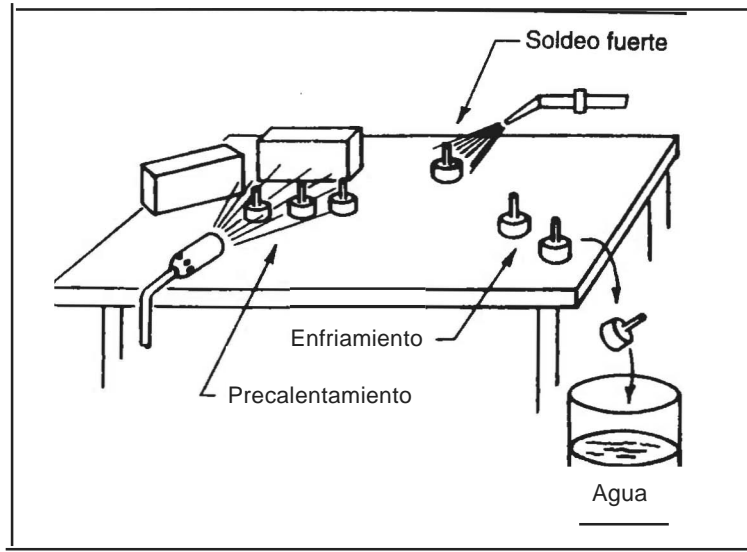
SOLDEO FUERTE DE PIEZAS PEQUEÑAS
